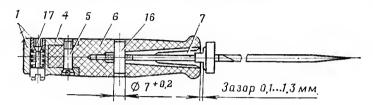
Замена рукоятки штыка-ножа: I — пружина защелки 1-7; 4 — наконечник 1-12; 5 — винт 1-5; 6 — рукоятка штыка-ножа 1-11; 7 — штык-нож Сб 1; 16 — стержень 1-9; 17 — винт зашелки 1-8
